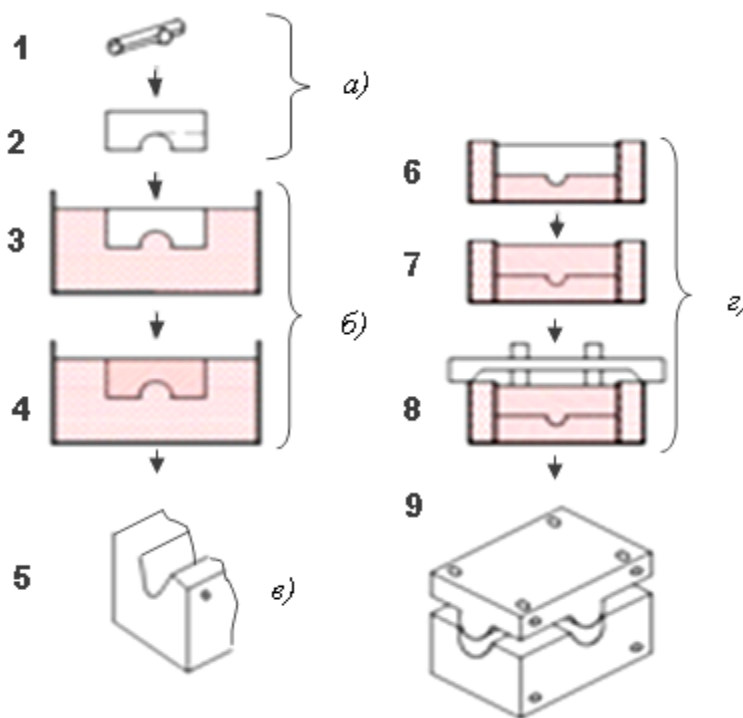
Технологическая схема изготовления свинцово-цинкового штампа:
